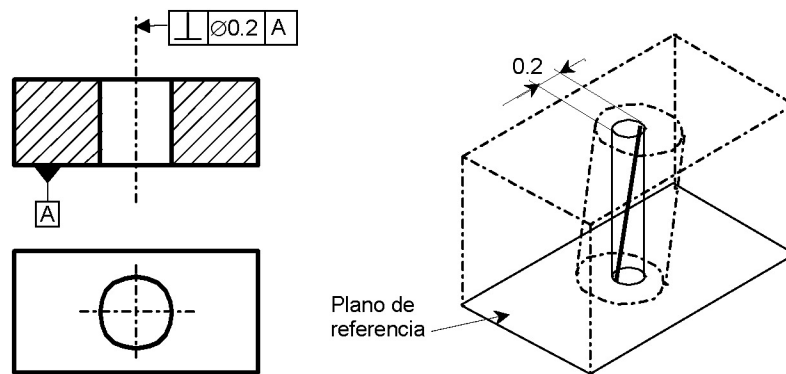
Zona de tolerancia cilíndrica al controlar la perpendicularidad de un eje
